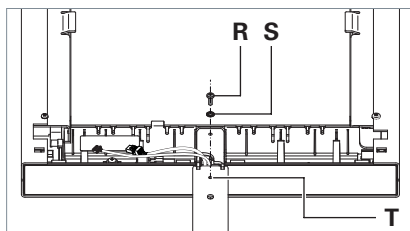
Fissaggio della testa dell'apparecchio d'illuminazione.
